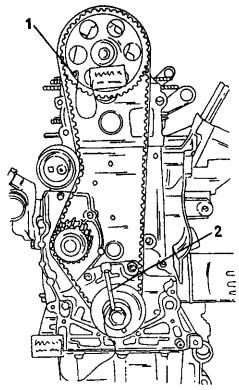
Вид спереди 8-клапанного двигателя. Сюда вставляется штифт для блокировки распределительного вала
